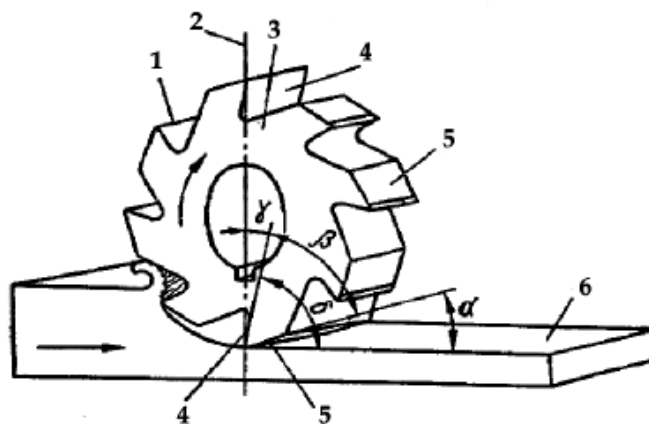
Геометрія фрези: 1 - різальна кромка; 2 - вертикальна площина; 3 - фреза; 4 – зуб фрези; 5 - задня поверхня зуба; 6 - оброблювана поверхня; а–
